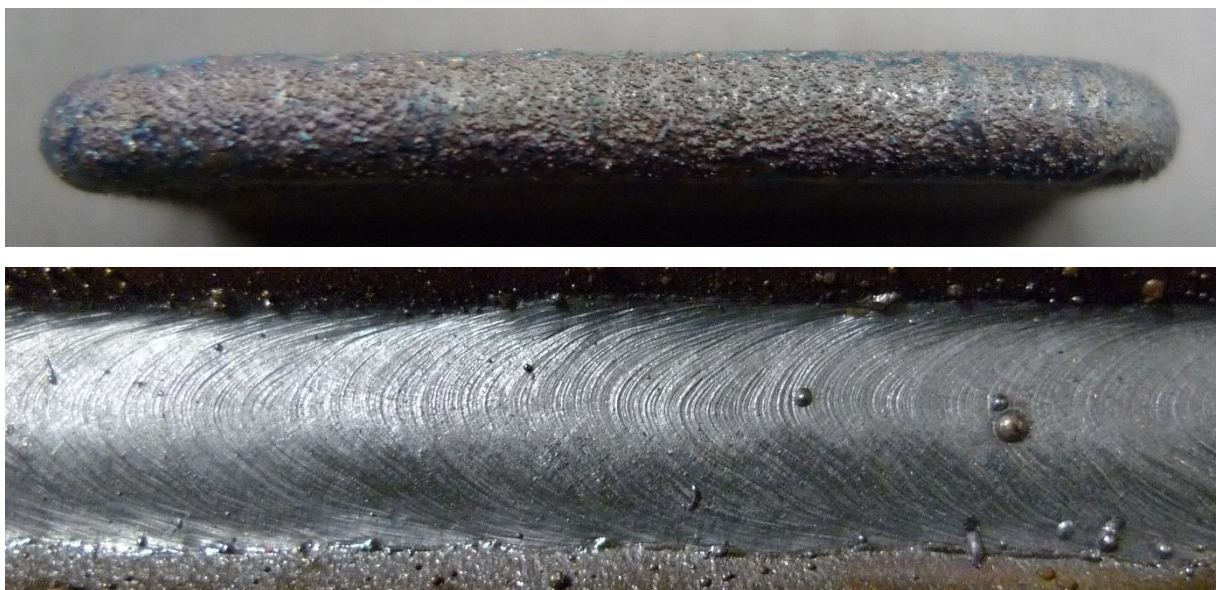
Oben: Laserauftraggeschweißte Wand aus Titan, Unten: MAG geschweißte Kehlnaht aus Stahl
